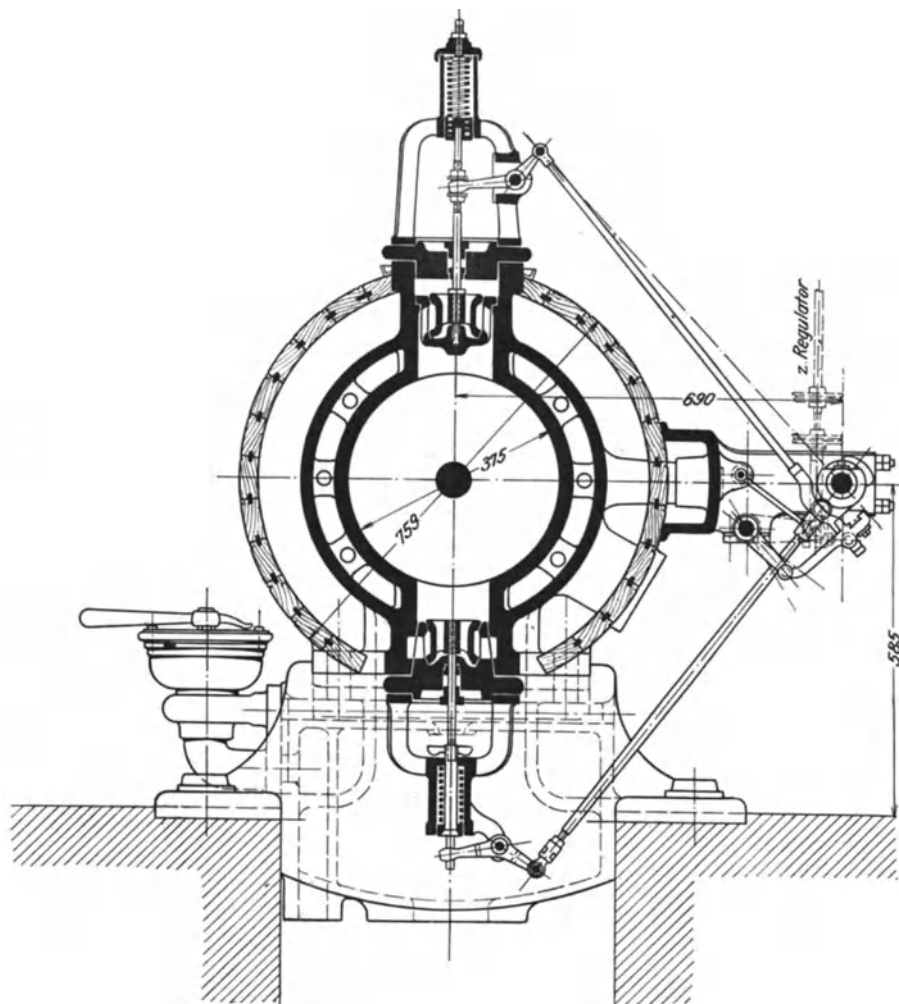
Zylinder und Steuerung zur Sulzermaschine 1866.
